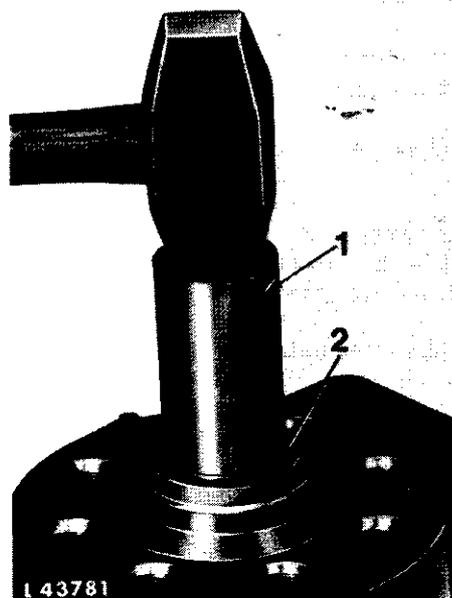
Pose du joint et du circlip de l'arbre de pompe
